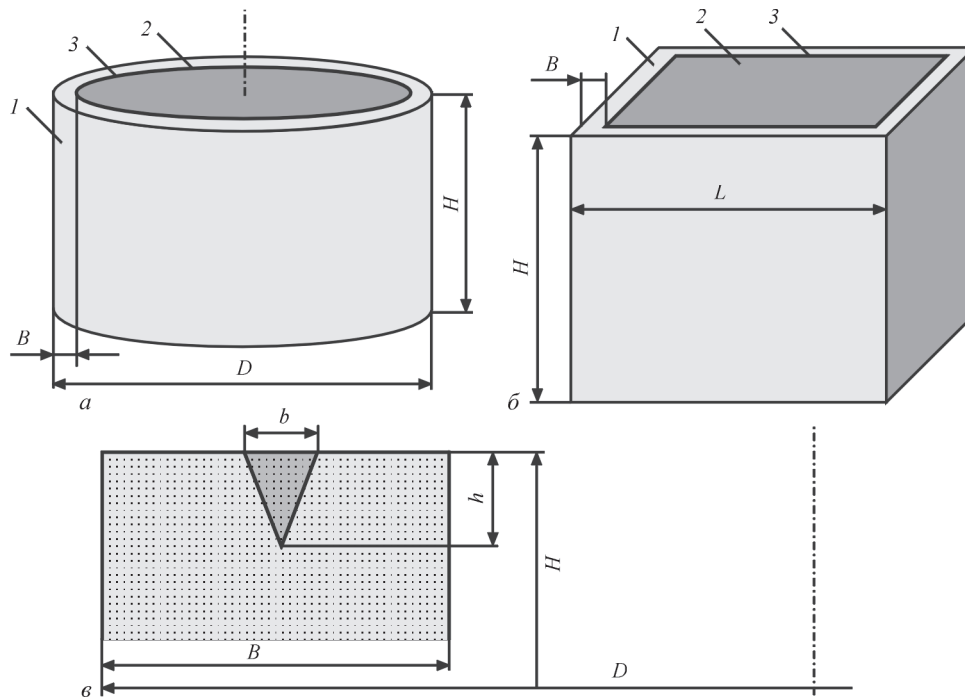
Геометричні параметри деталей, що зварюються, і лазерного провару (темна трикутна ділянка): 1 – корпус; 2 – фланець, що приварюється; 3 – зварний шов
